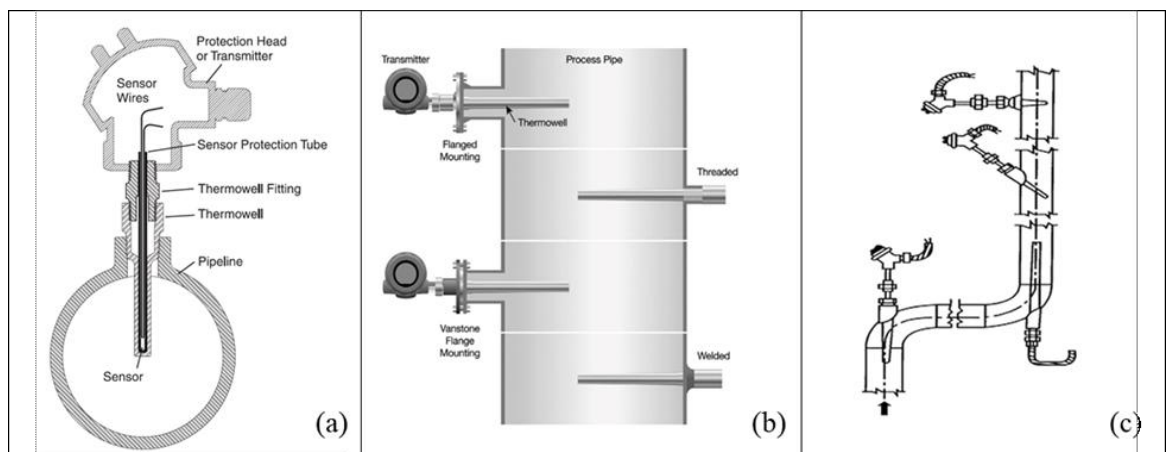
Condizioni di installazione dei pozzetti: a) assemblaggio sonda-pozzetto; b) connessione pozzetto-condotto; c) posizionamento pozzetto
